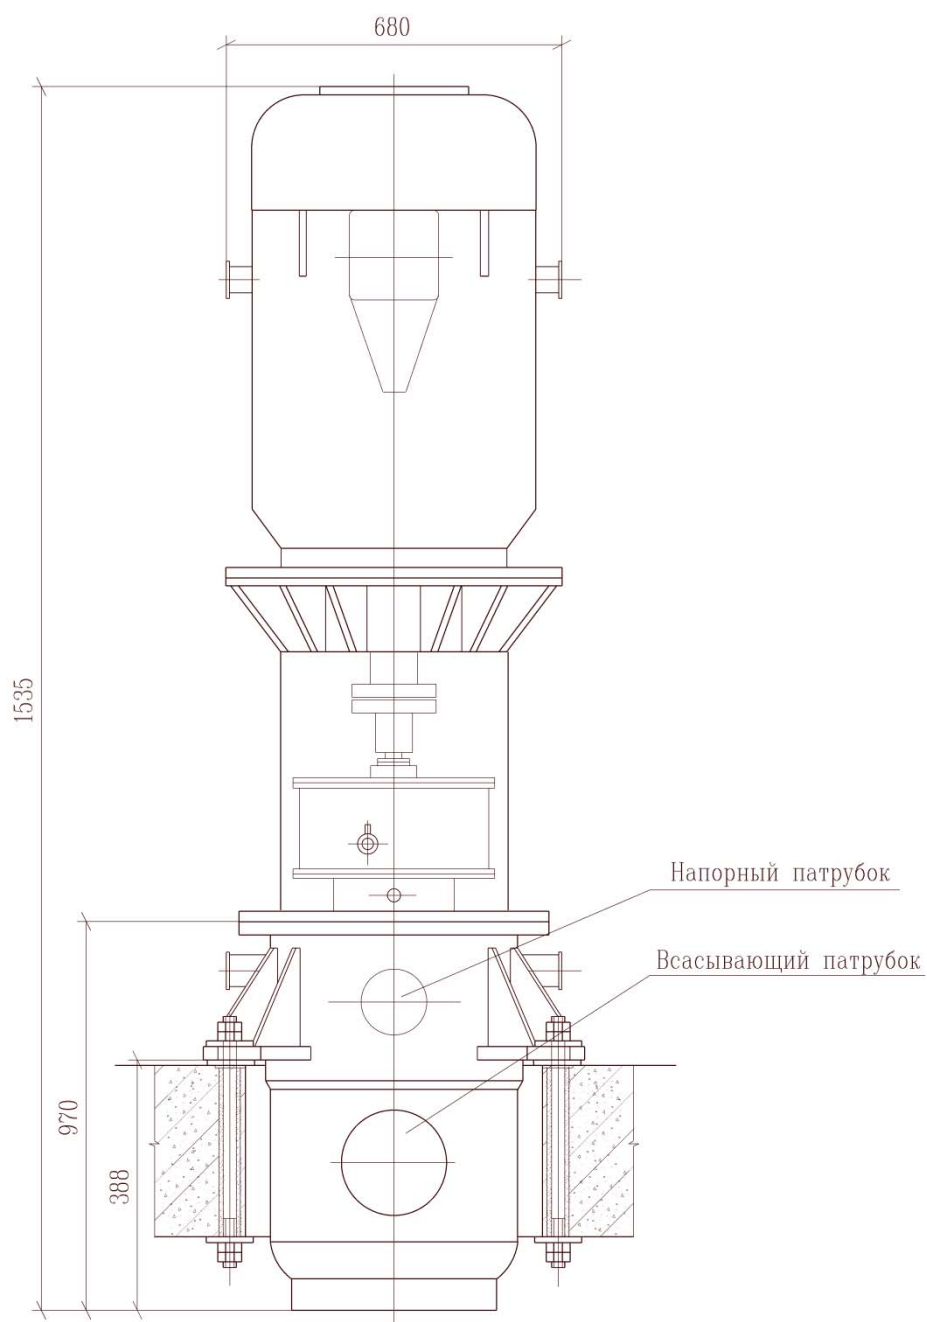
Габаритный чертеж насоса бака сбора отмывочных вод
